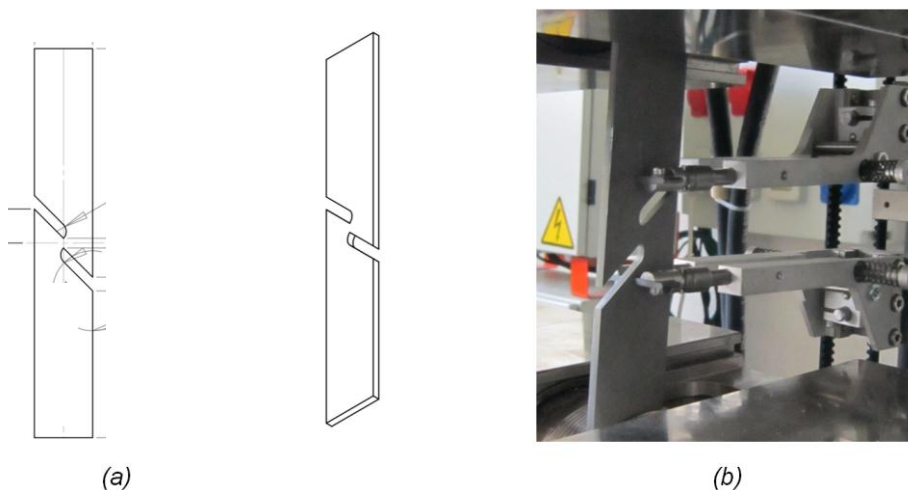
Epreuve de cisaillement: (a) forme et dimensions de l'éprouvette et (b) montage de l'éprouvette sur la machine de traction
